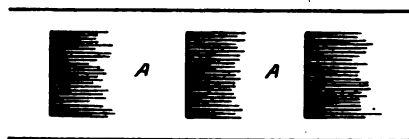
Fleckenbildung auf einem Synchronmaschinen-Schleifring.
